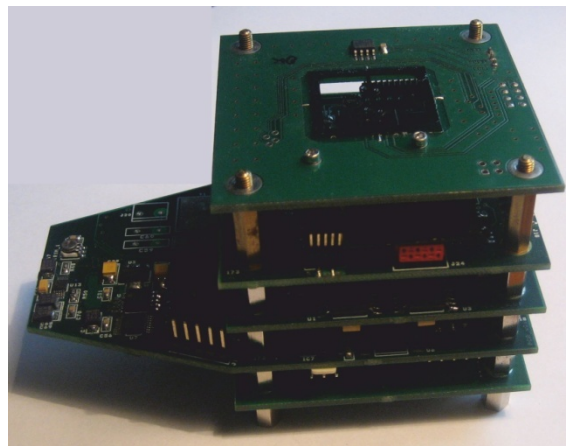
a Obr. 3-21 Realizovaný Chip Carrier modul (horní PCB) spolu s optickým systémem a předzesilovačem PZ1 (pod horní PCB)
